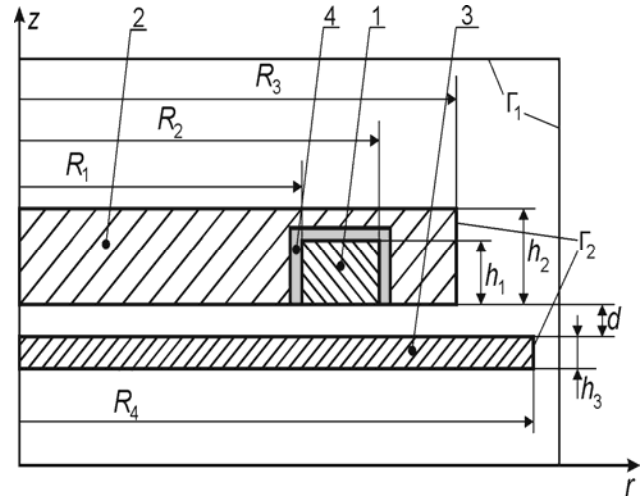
Розрахункова схема індуктора разом із заготовкою.
